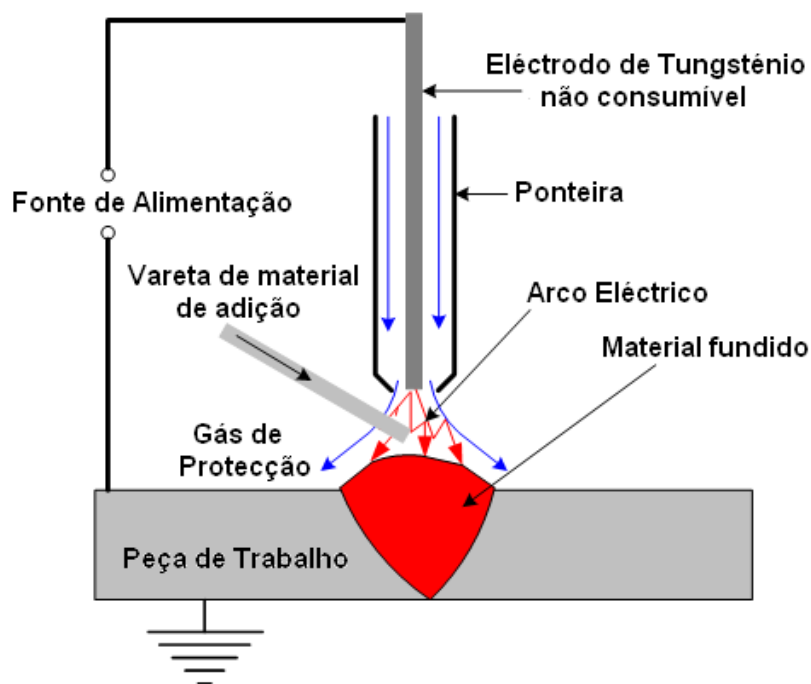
Processo de soldadura TIG [3].
